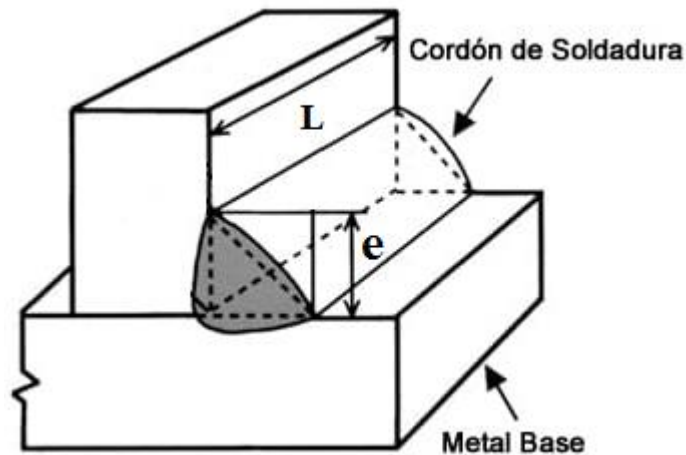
dimensiones del cordón de soldadura. (Kobelco, n.d.)
